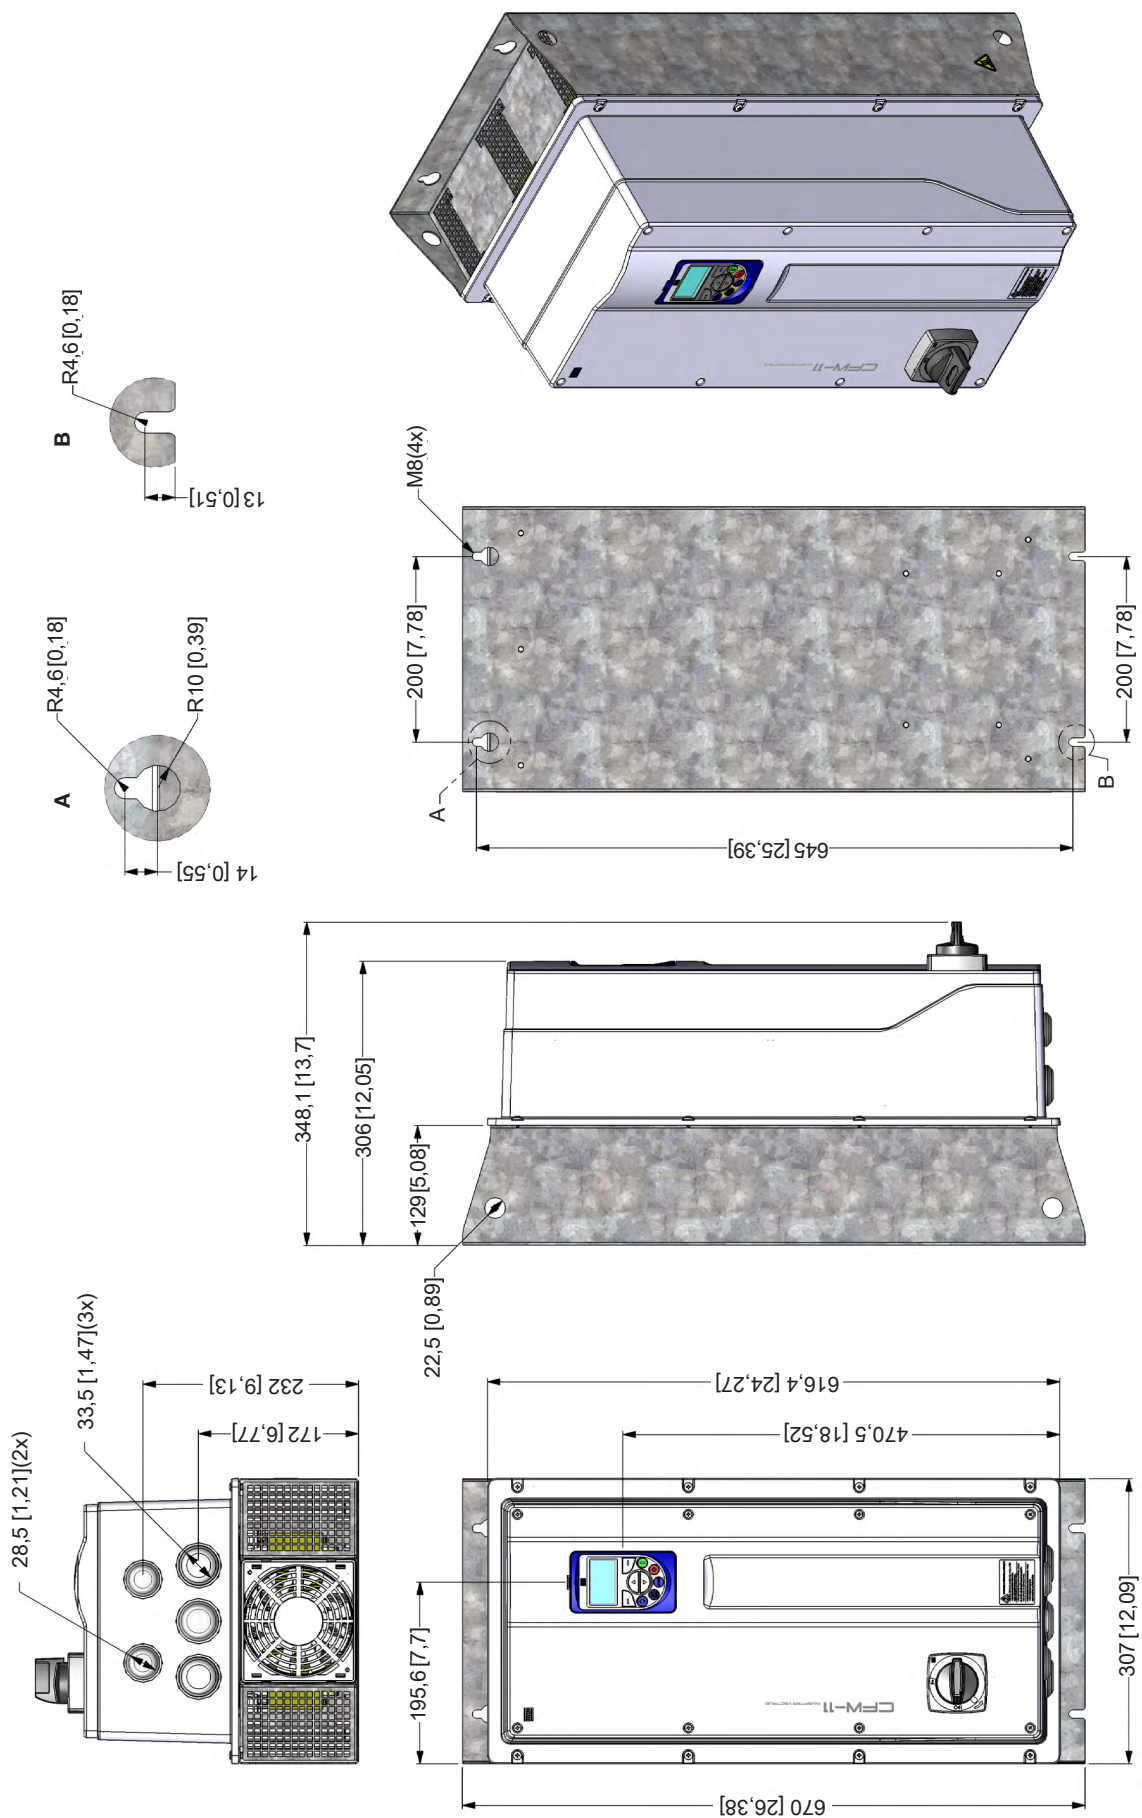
Габаритные размеры преобразователя, размер корпуса C, мм [дюйм.]
